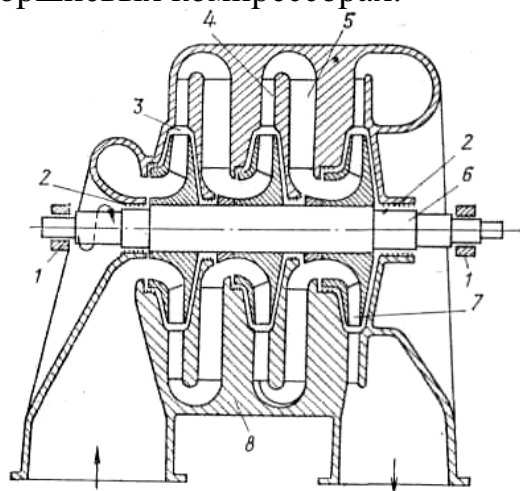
Схема многоступенчатого центробежного компрессора:
